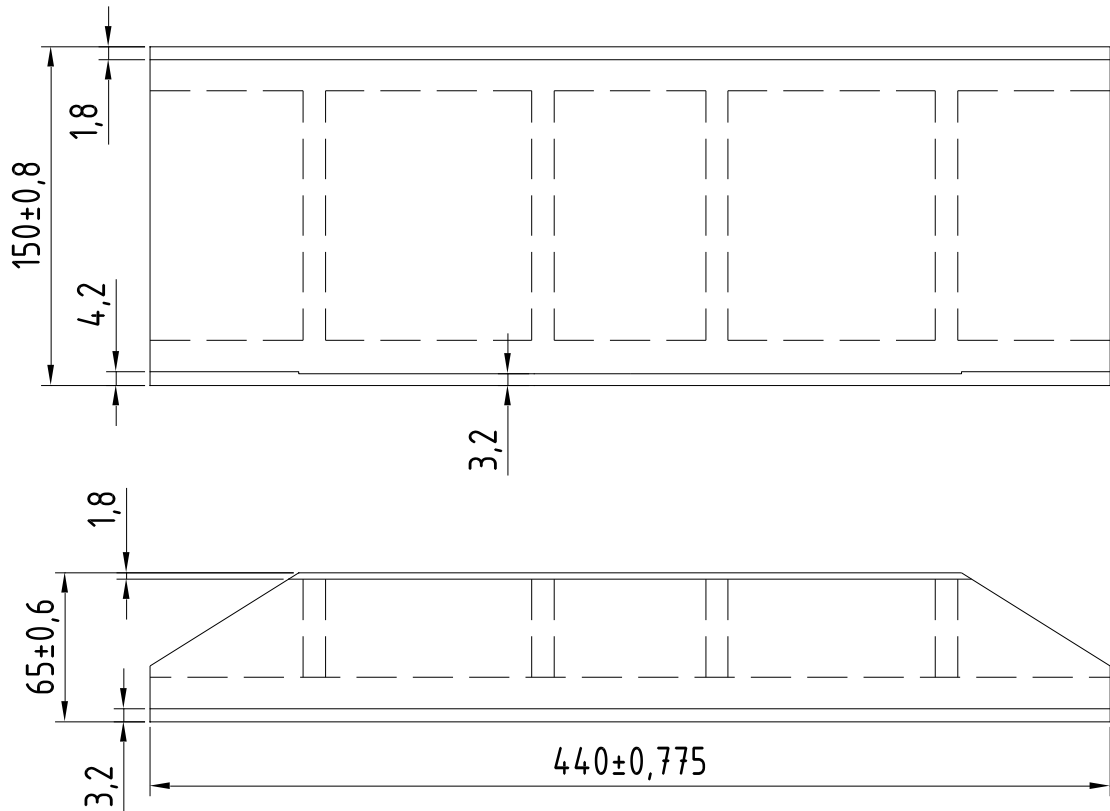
Заготовка корпусу 1032/1 з визначеними припусками та допусками
